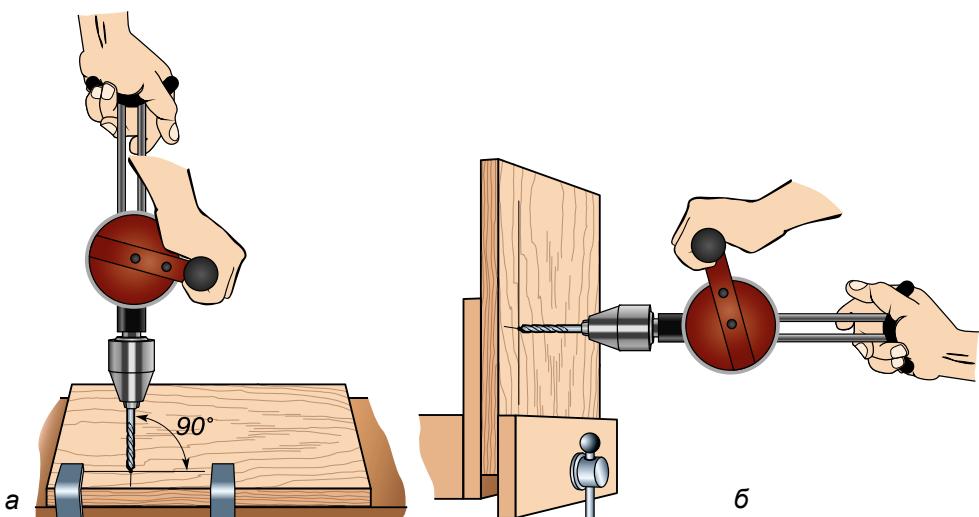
Сверление отверстий дрелью: а – горизонтальных; б – вертикальных
